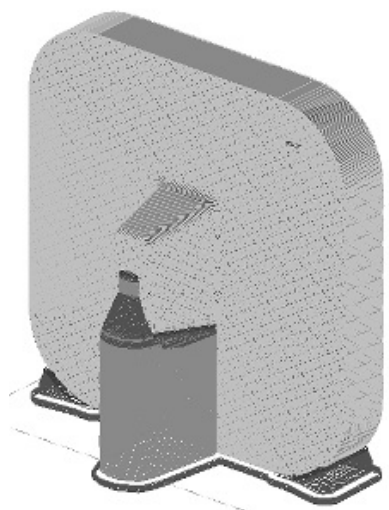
Disposição de construção do inserto macho na máquina de prototipagem rápida.
